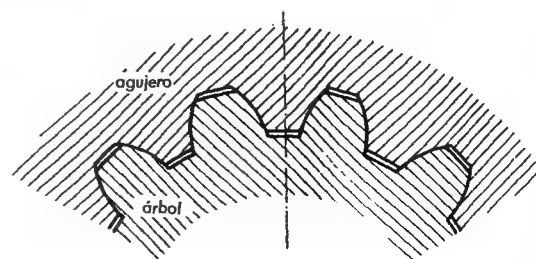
Embrague de dientes Stub, tipo engranaje.
